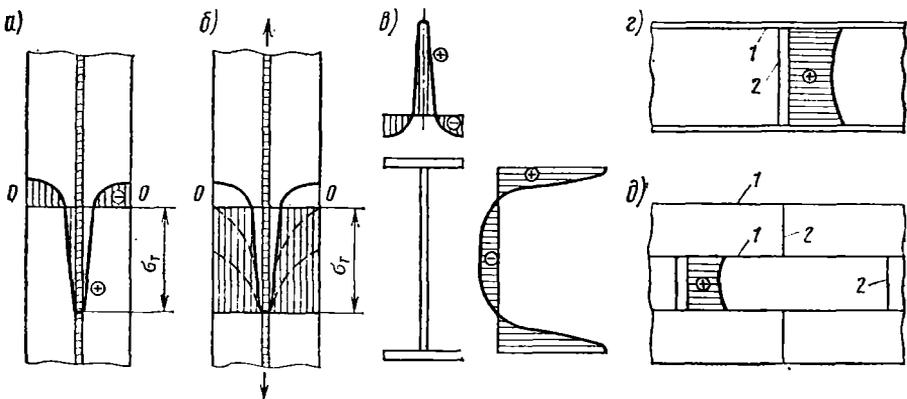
Эпюры внутренних напряжений от сварки:
